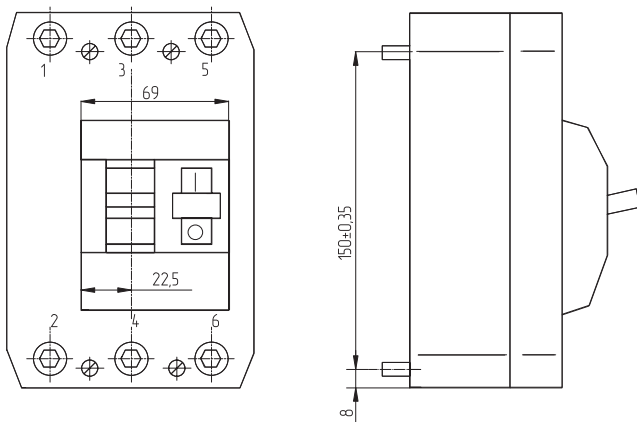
Габаритные, установочные размеры, масса выключателя типа ВА04-36 стационарного исполнения
